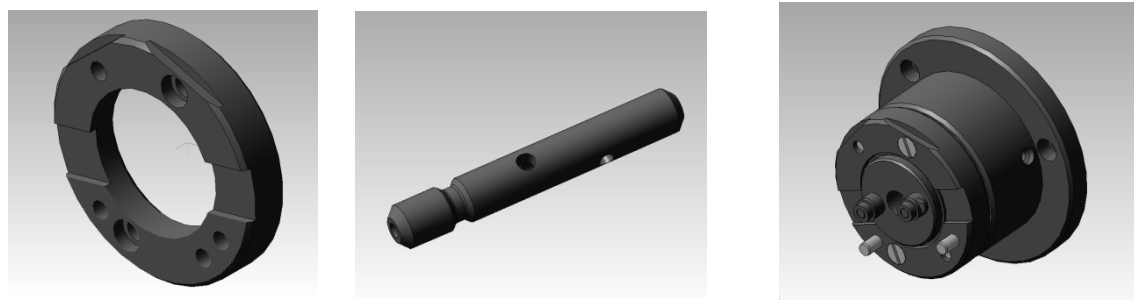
3D-модели отдельных деталей и всего приспособления
